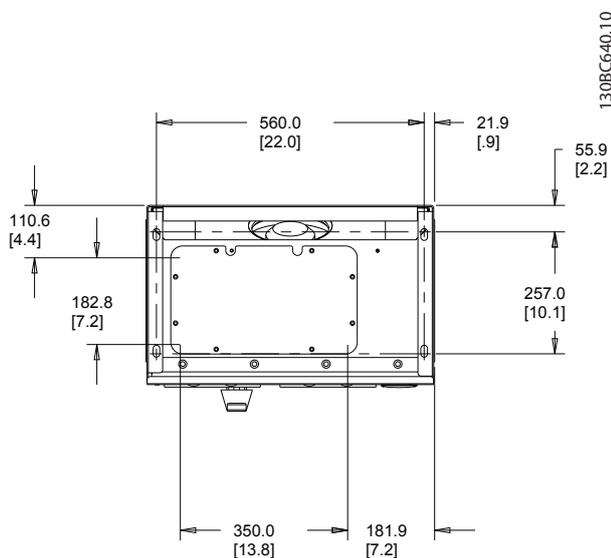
Gabinete metálico tamanho D14, vista inferior
